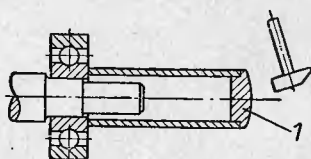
Монтаж подшипника на вал с помощью монтажной трубы.
